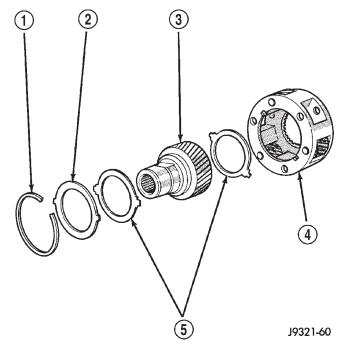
Componentes de los engranajes impulsor y de escala de baja
